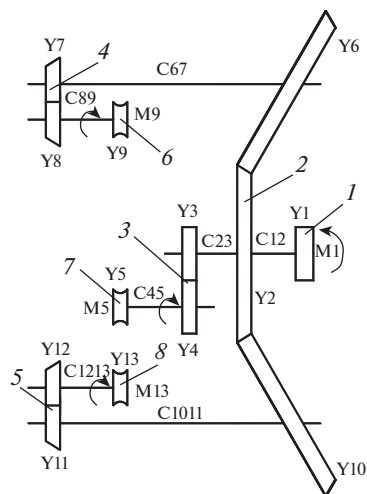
Кинематическая схема привода клетки скобы 1 – электродвигатель, 2 – тройной конический редуктор, 3 – цилиндрический редуктор, 4, 5 – двойной конический редуктор, 6, 7, 8 – прокатный валок, Y1, Y2, ..., Y12 – момент инерции масс на валах, C12, C23, ..., C1213 – коэффициент жесткости участков валов, M1, M2, ..., M13 – внешний момент, приложенный к массам на участках валов.
